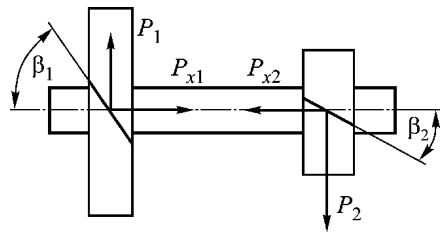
Схеми сил, що діють на зубчасті колеса проміжного вала коробки передач
